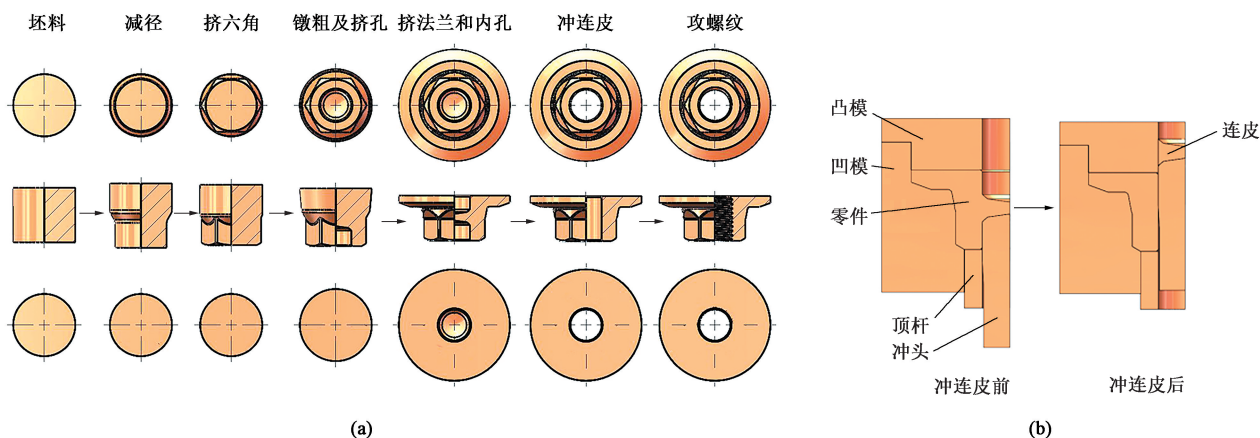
大法兰螺母的多工位成形工艺 (a) 和冲连皮过程简图 (b)
